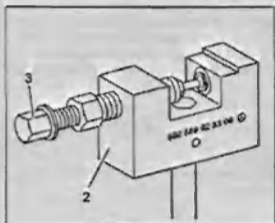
Соберите приспособление 2 для рассоединения цепи и упорный шпindel 3.
